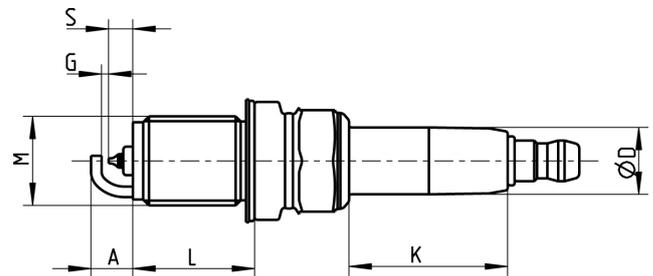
Dimensionen der Zündkerze Typ 6118B...
